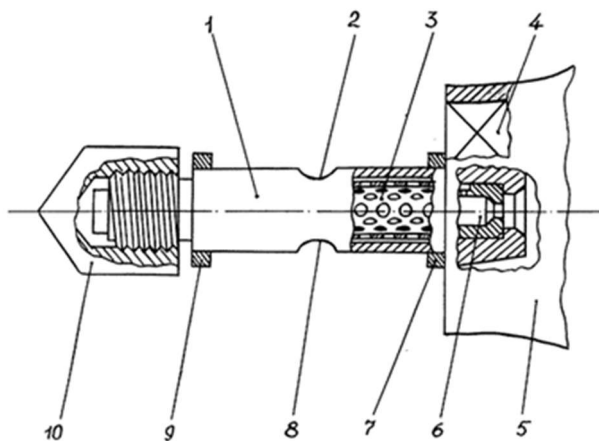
Конструктивная схема (в разрезе) штатной топливной форсунки ВРД марки НК-8-2У
